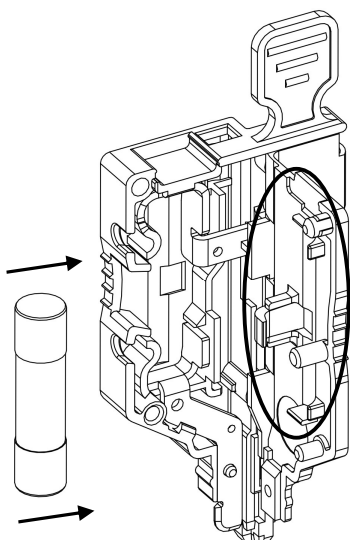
установка защитного предохранителя размером 5x20 мм в паз держателя
